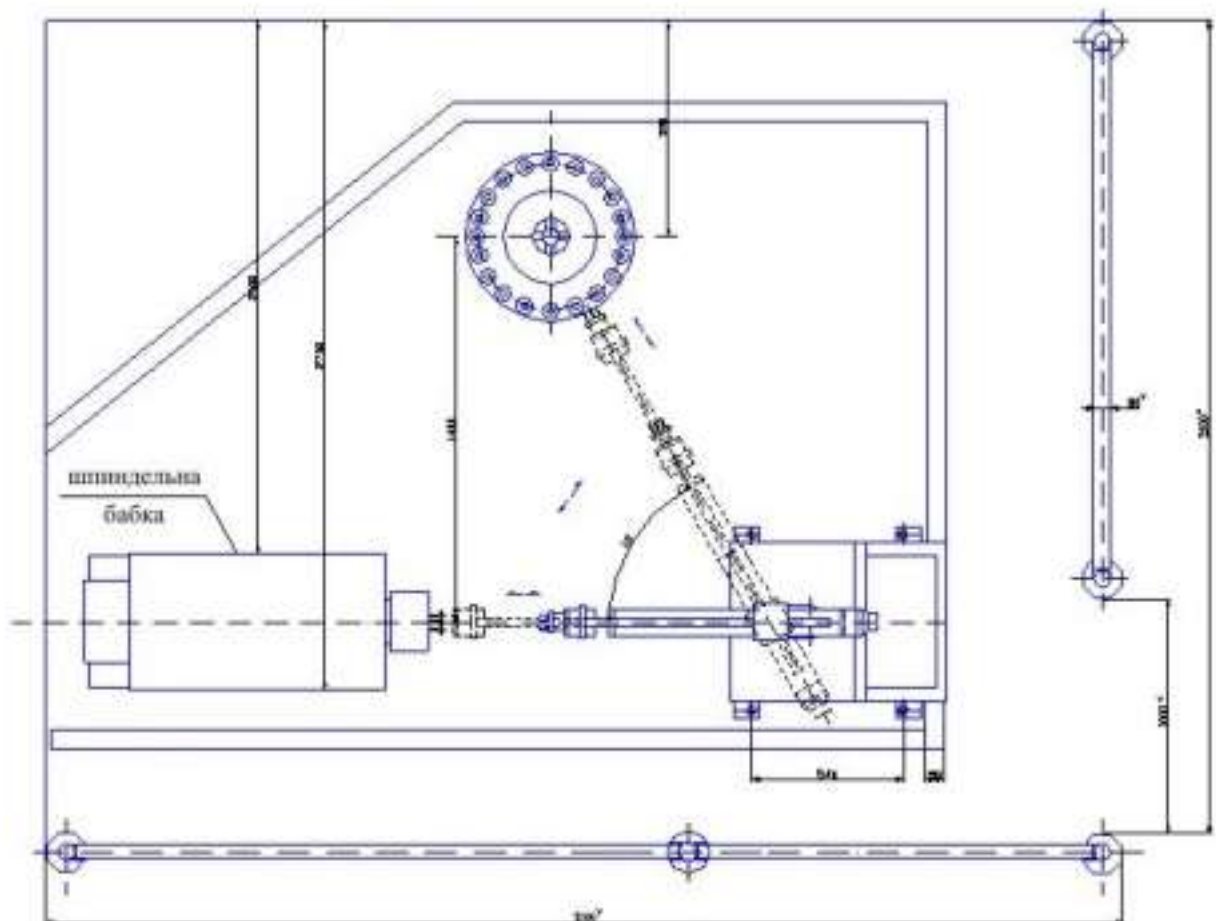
Загальний вид лабораторного стенда-макета верстатного модуля
